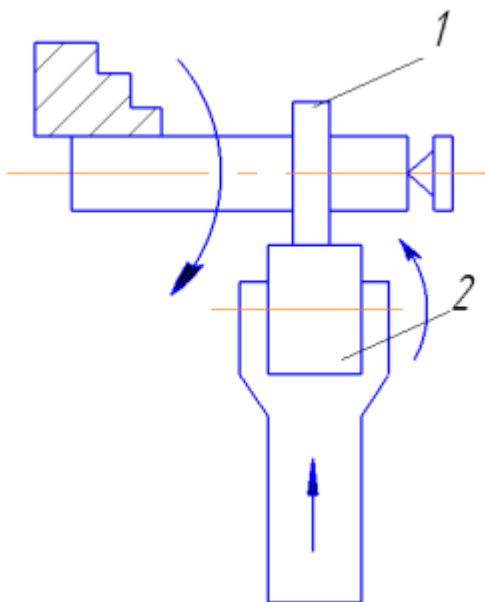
Схема обкатывания поверхности роликом : 1-обрабатываемая поверхность; 2-ролик
